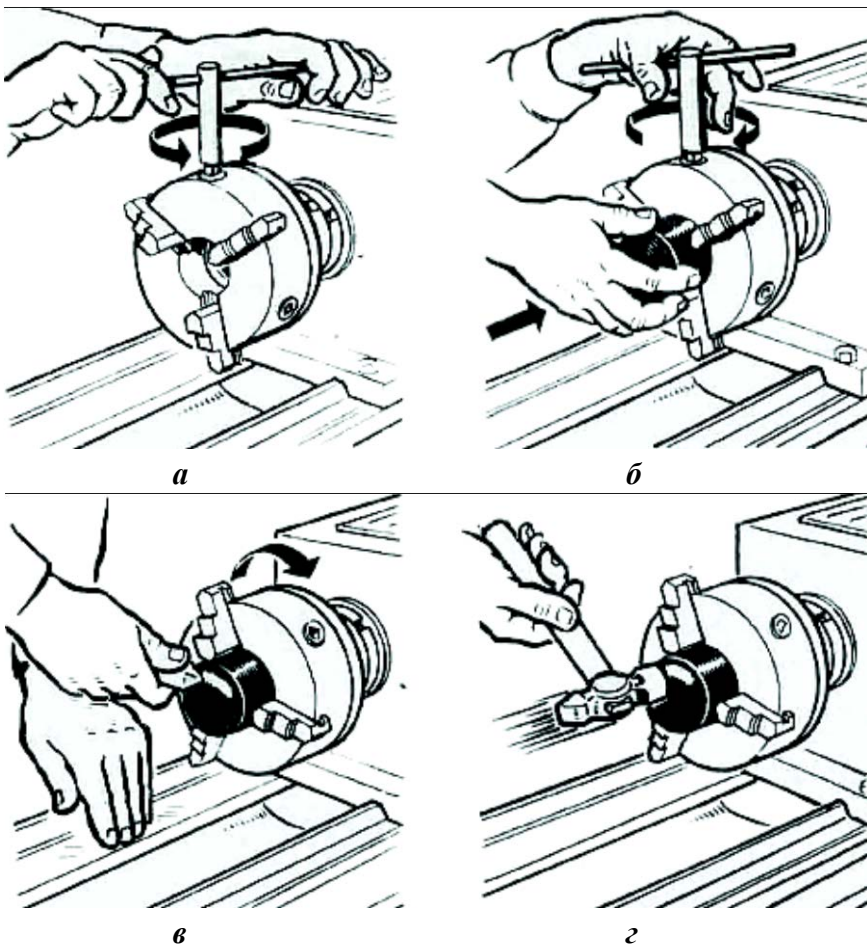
Прийоми установки заготовки в трикулачковому патроні
